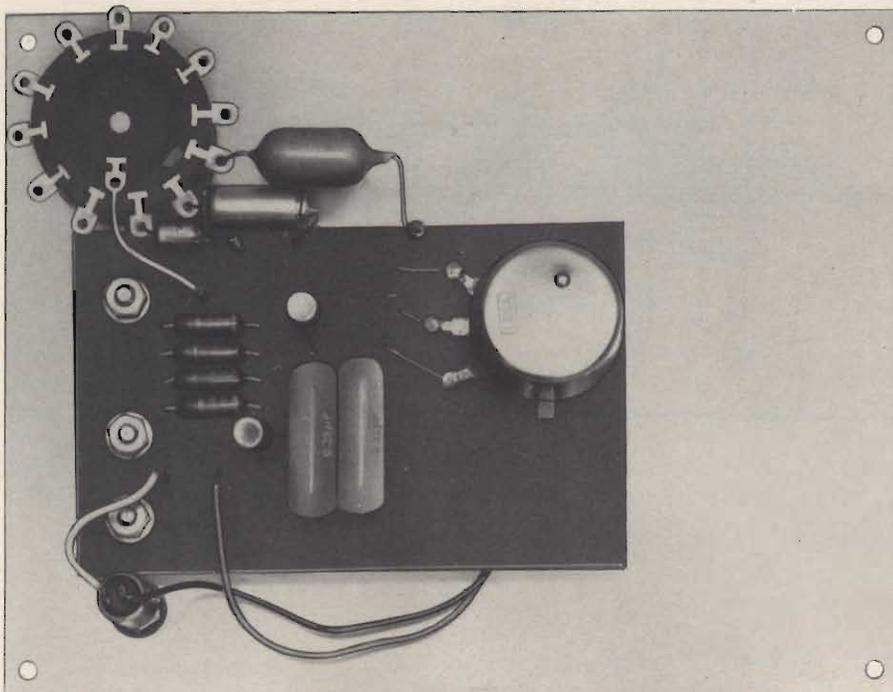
Aspetto del capacimetro UK/440 a montaggio ultimato visto dal lato dei componenti.
